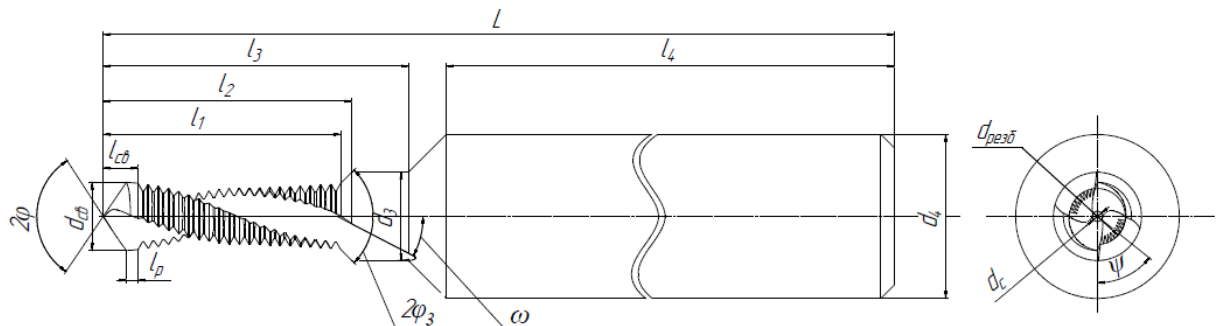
Сверло-резьбофреза для обработки резьбы М3х0,5.
